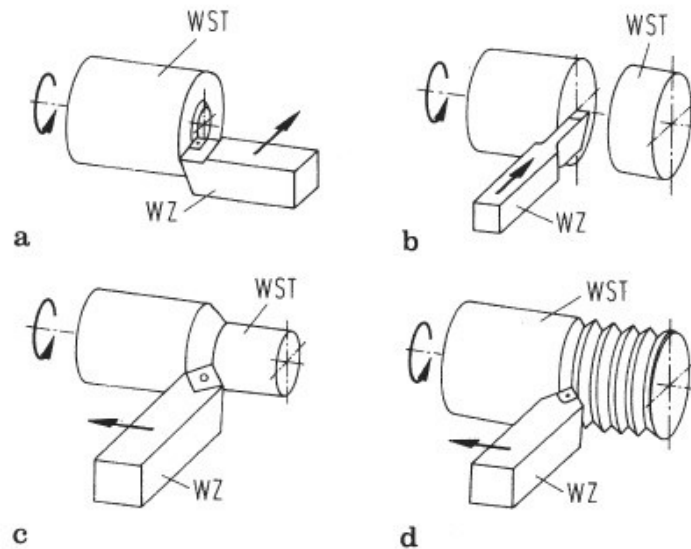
Drehverfahren. WST: Werkstück, WZ: Werkzeug
